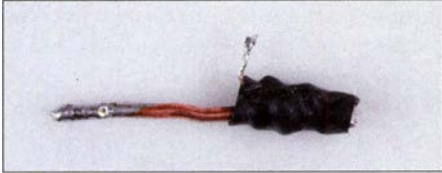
Mit Schrumpfschlauch geschütztes Bauelement vor dem Einbau in den Stecker
